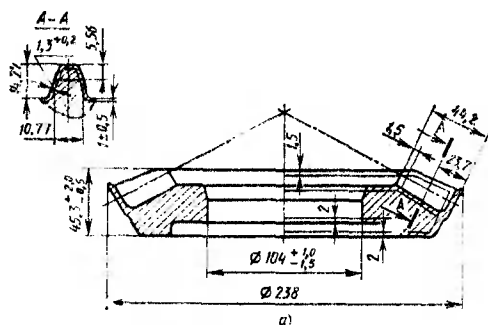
Штамповка конических колес с круговыми зубьями:
